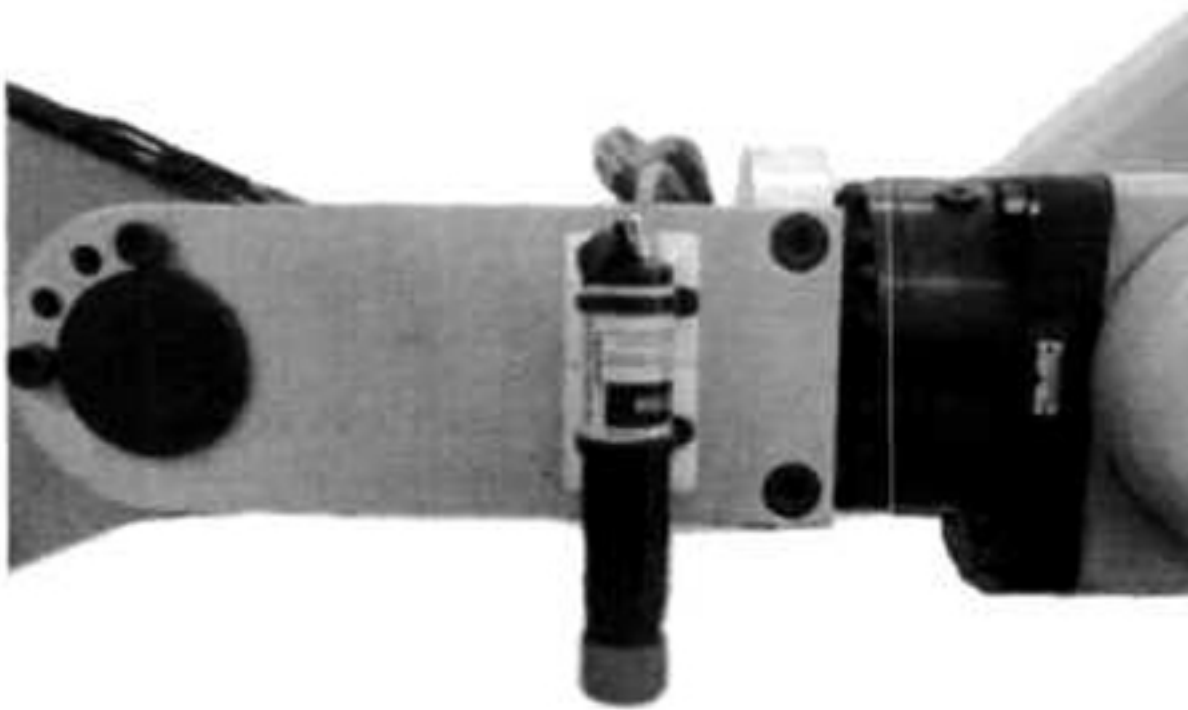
Apuntador láser colocado en la estructura móvil del manipulador
